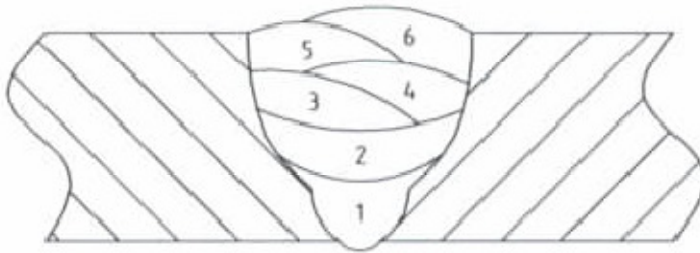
Lagenaufbau einer Schweißverbindung
